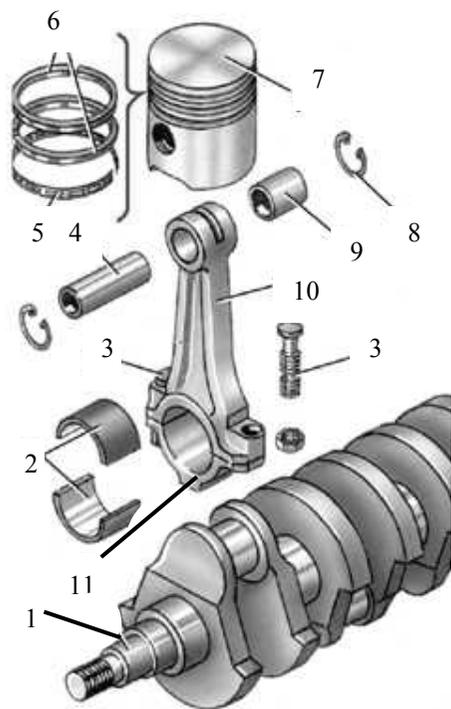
Коленчатый вал и детали шатунно-поршневой группы:
